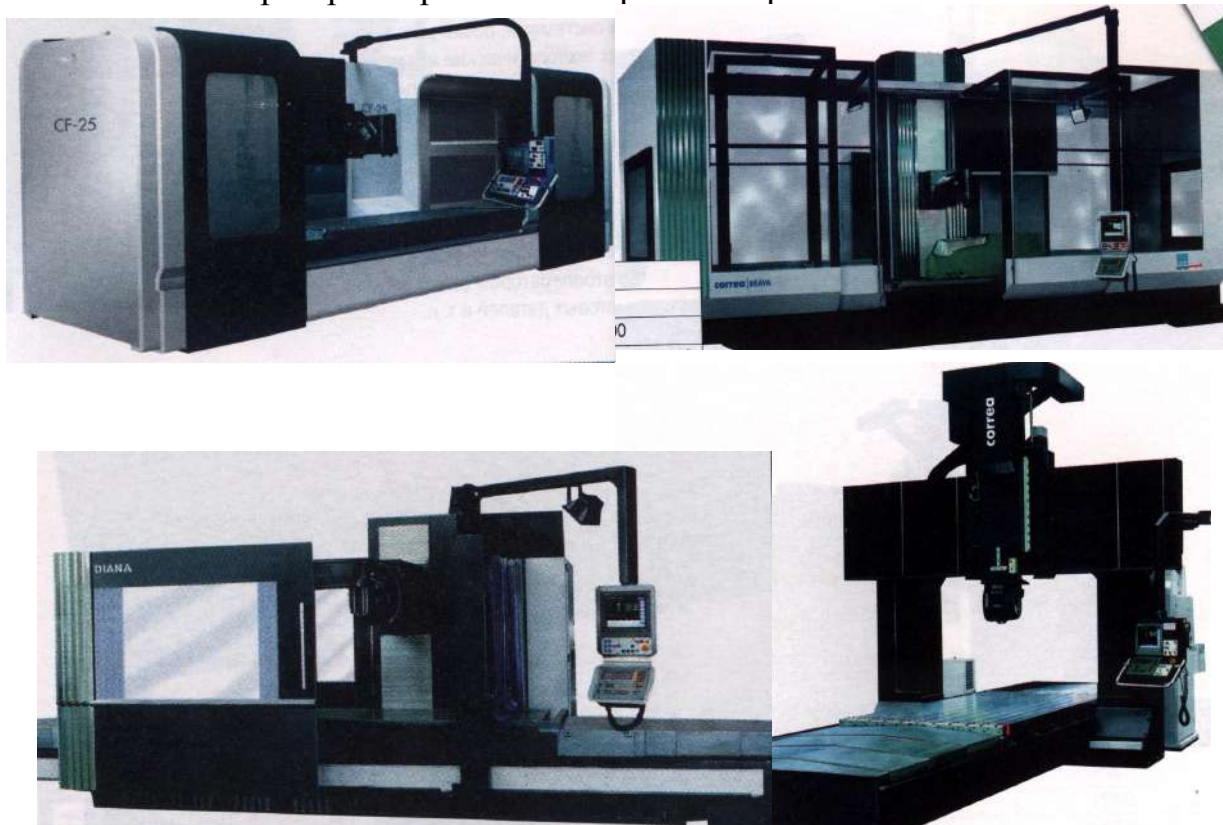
Модельний ряд фрезерних верстатів фірми CORREA
